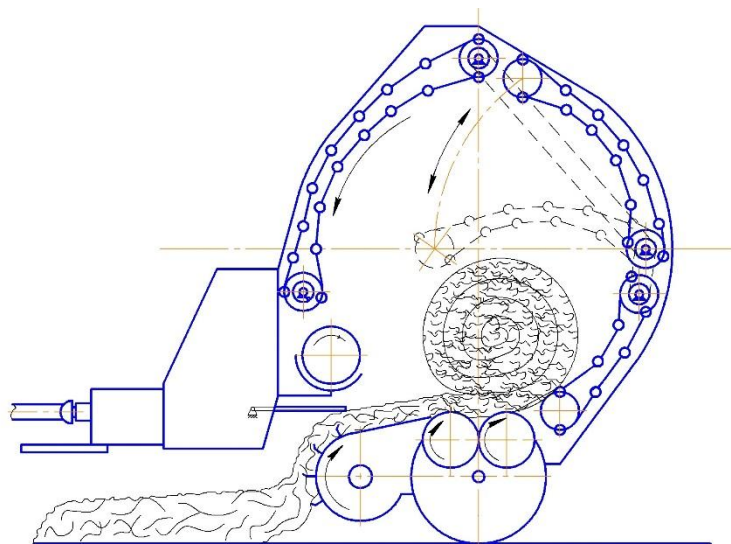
Схема модернизированного пресс-подборщика с цепочно-роликовым прессовальным контуром
